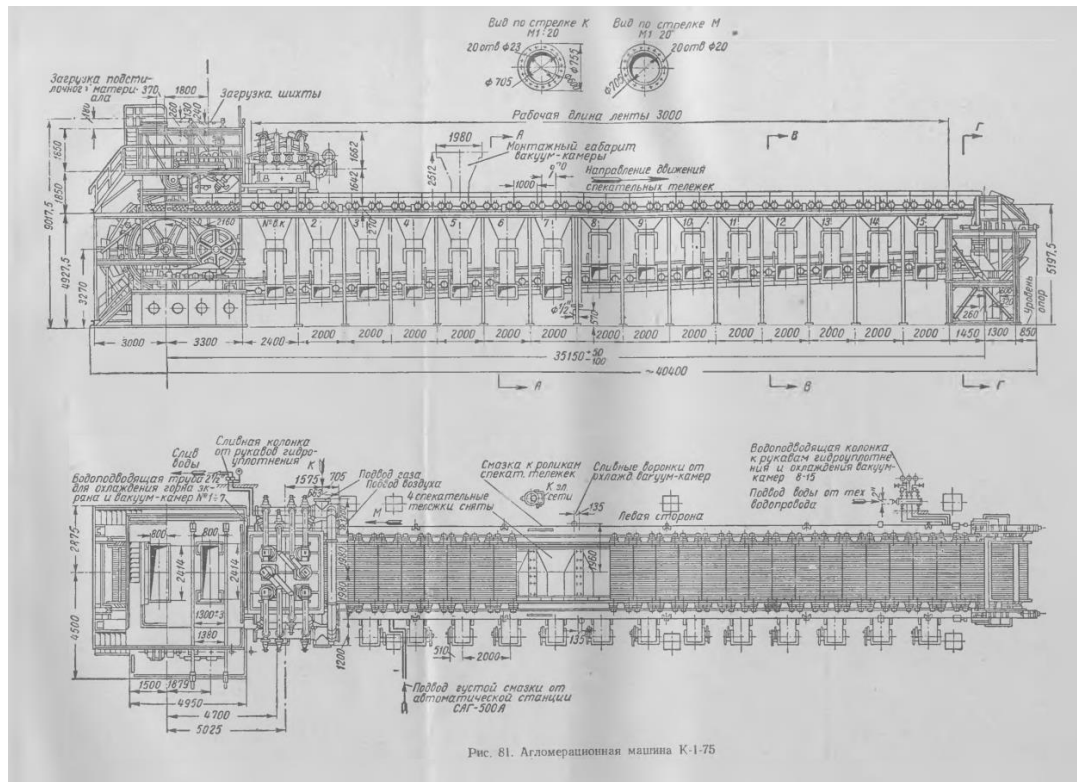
Загальний вигляд агломераційної машини К-1-75
